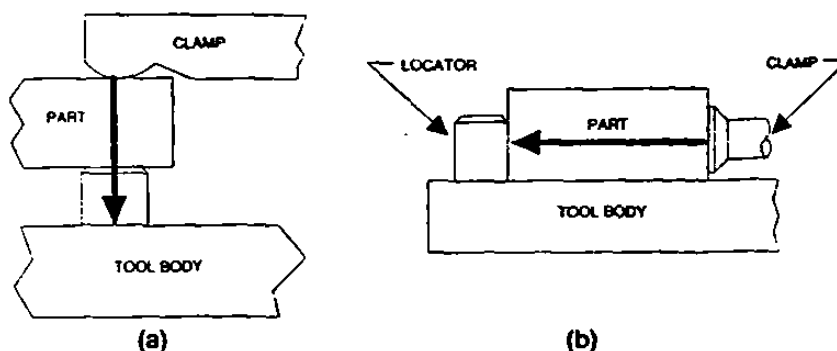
Las mordazas tienen que ser siempre posicionadas así que las fuerzas de sujeción son dirigidas a los soportes o posicionadores.
